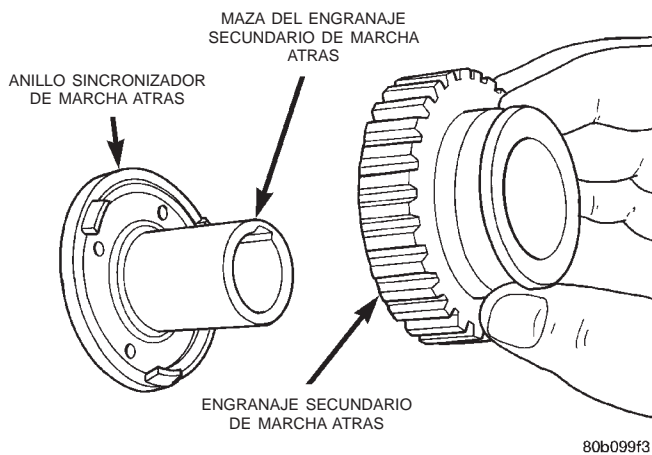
Desmontaje del engranaje secundario de marcha atrás
